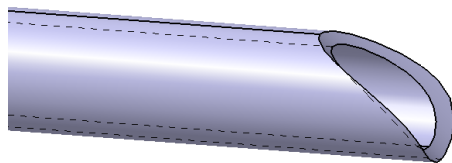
Maquette CATIA d’un tube avec gueule de loup.
